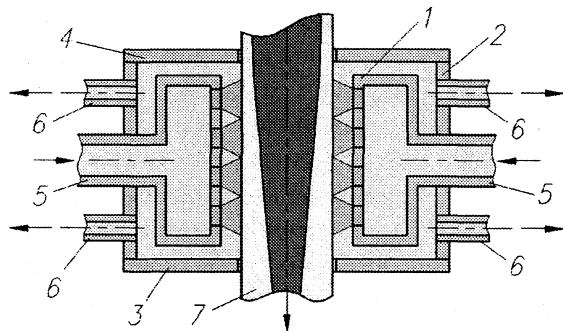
Схема устройства струйного вторичного охлаждения слитка: 1 – коллектор; 2 – кожух; 3 – фланец нижний; 4 – фланец верхний; 5 – патрубков подводящий; 6 – патрубков отводящий; 7 – слиток
